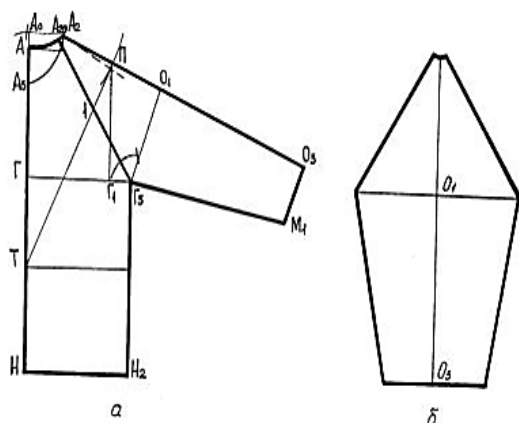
Чертеж конструкции спинки, переда (а) и рукава реглан (б) регулярного трикотажного изделия свободной формы
